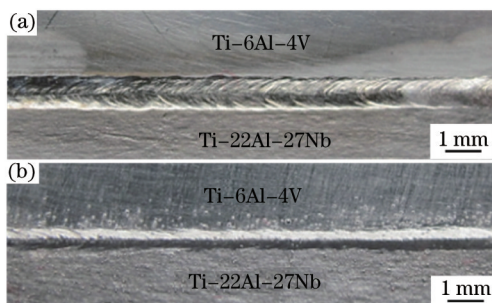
焊缝表面成形。(a) 焊缝正面;(b) 焊缝背面
